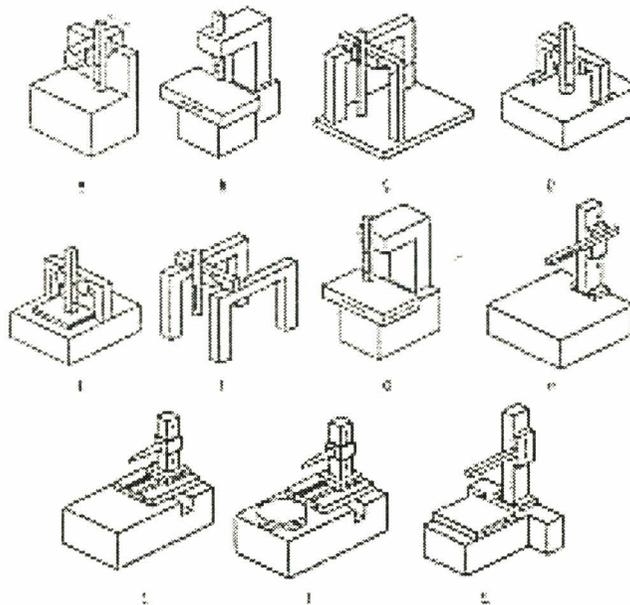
Diversas arquitecturas de MMC (de arriba abajo y de izquierda a derecha): cantilever con mesa fija, cantilever con mesa móvil, puente en forma de L, puente móvil, puente fijo, tipo pórtico (gantry), de columna, de brazo horizontal, con cabeza móvil, de brazo horizontal y mesa fija, de brazo horizontal y mesa fija con plato giratorio, de brazo horizontal y mesa móvil. UNE-EN ISO 10360 1, 2001.
